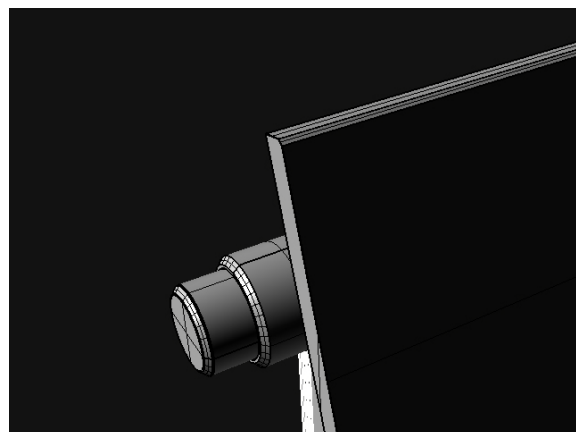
Tvarovaná deska - přední pohled - finální render
